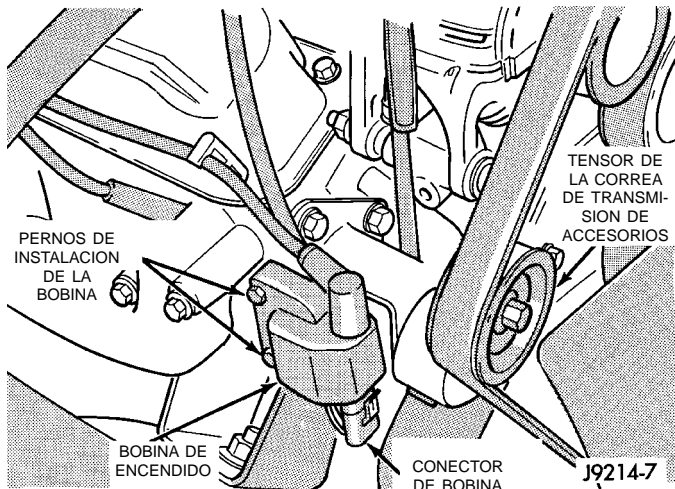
Bobina de encendido—Motor de 5.2L/5.9L V-8
